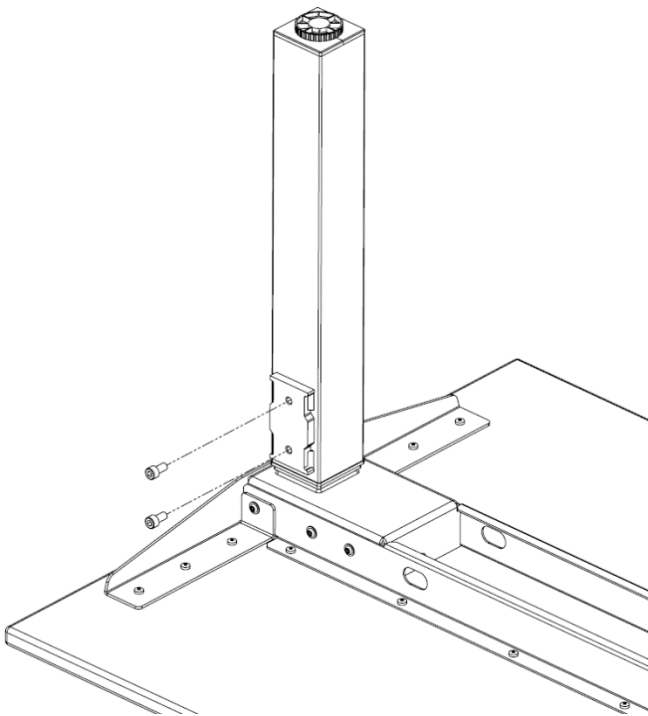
Vormontage der Innensechskantschrauben M8x16
